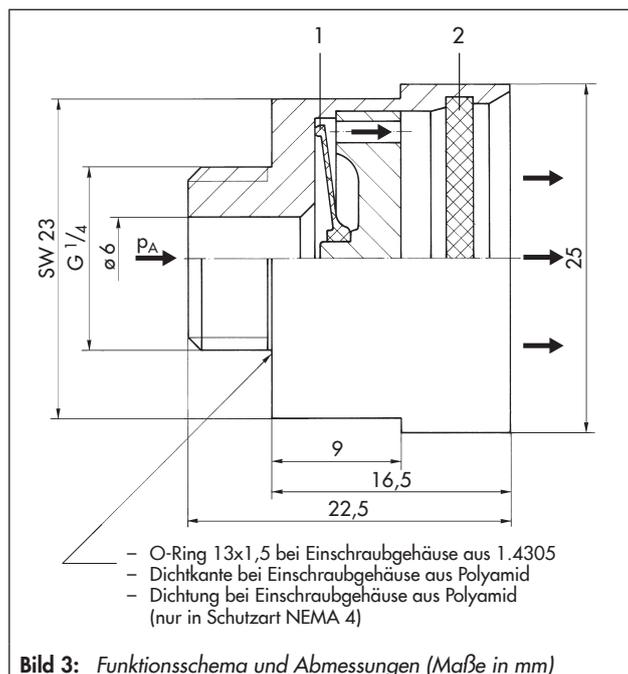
Funktionsschema und Abmessungen (Maße in mm)
